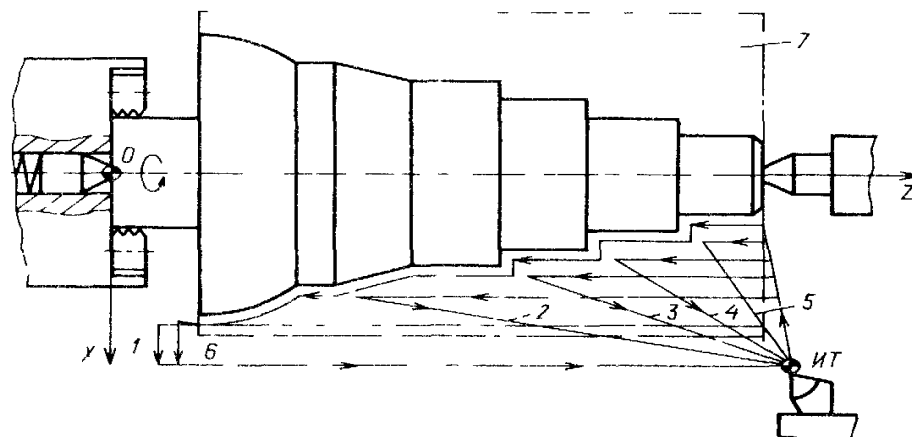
Обтачивание заготовки вала на токарном станке с ЧПУ:
